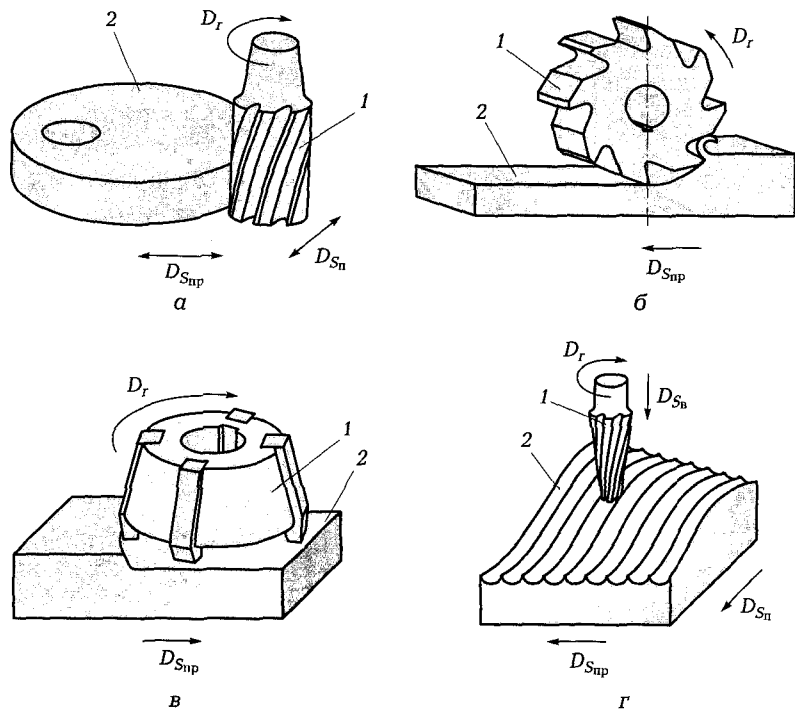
Схемы формообразования поверхностей фрезерованием: а — концевой фрезой; б — цилиндрической фрезой; в — торцевой фрезой; г — фасонной концевой фрезой; 1 — инструмент; 2 — заготовка
